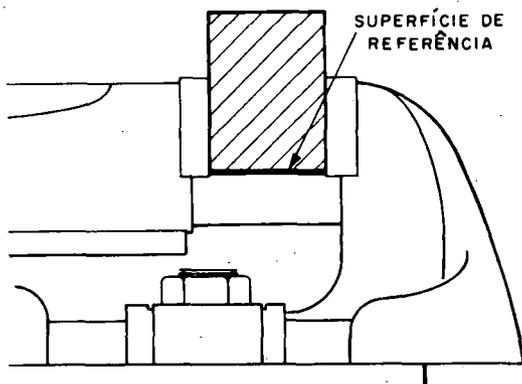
Superfície de referência do material (SR) apoiada na base da morsa para obter, com a fresagem, uma superfície paralela.
